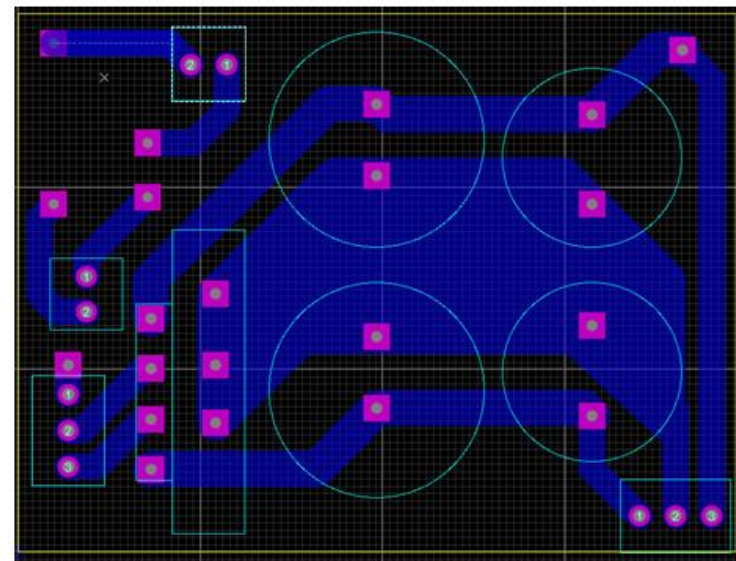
Diseño de PCB para fuente de alimentación.
